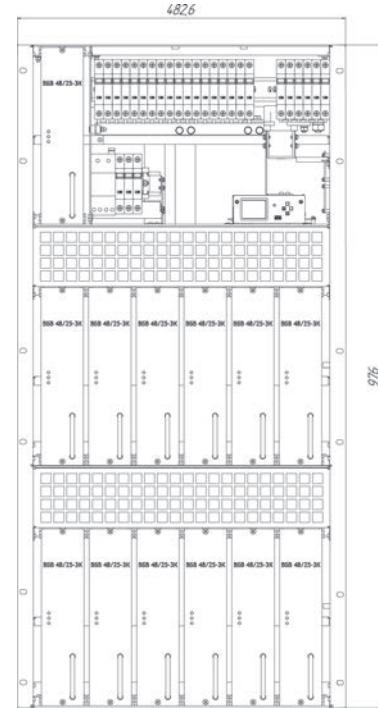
Габаритный чертеж УЭПС-3К 60/260, УЭПС-3К 48/325 (ВЭ)
